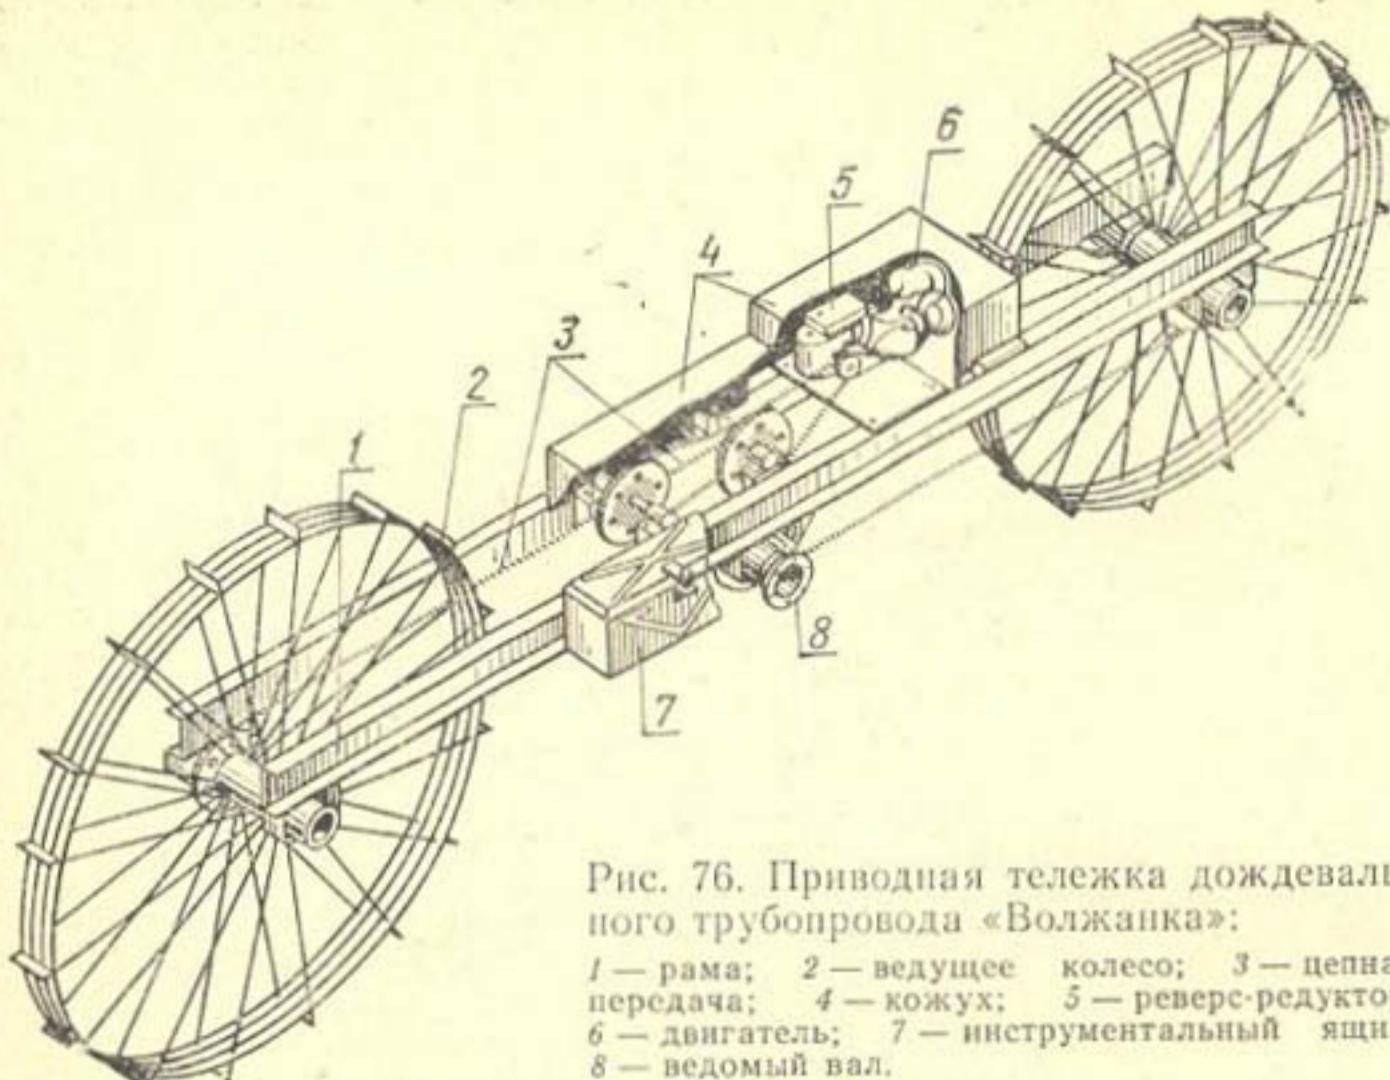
Приводная тележка дождевального трубопровода «Волжанка»:
